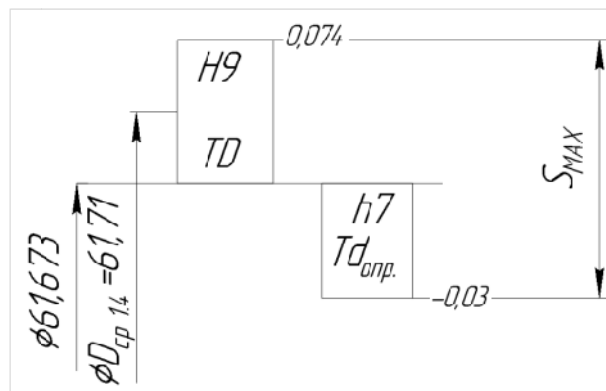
Посадка із зазором розтискної оправки та деталі
